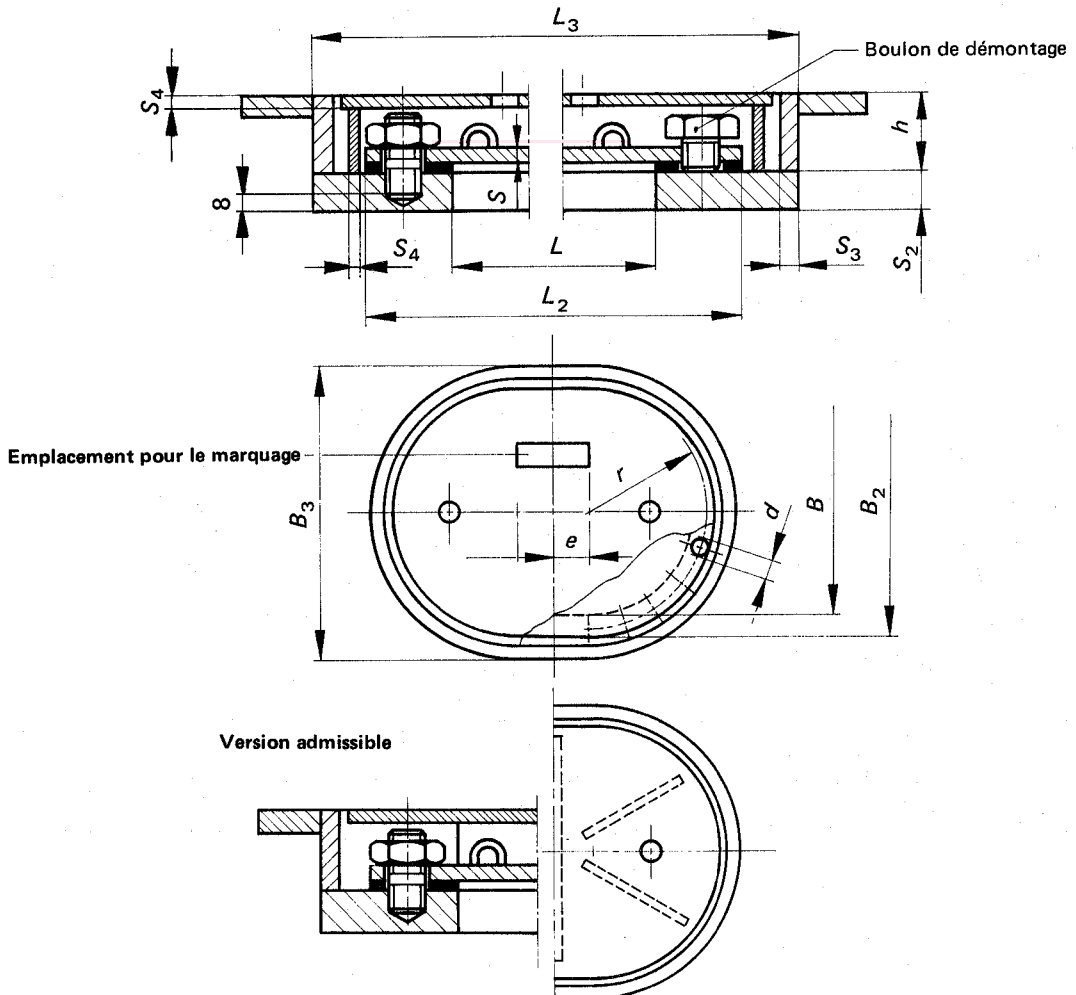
Forme et dimensions principales des trous d'homme, type D
